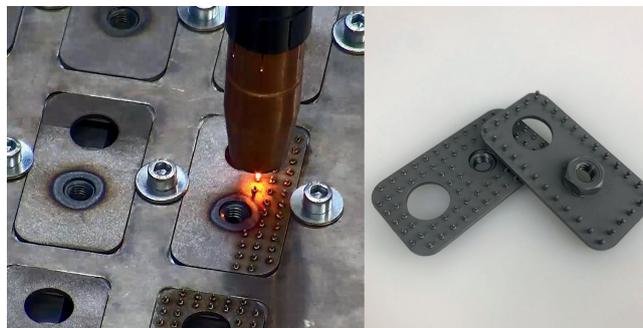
Durch CMT-Schweißen können auf den Gewindeeinlegern Pins in definierter Länge und mit verschiedenen Kopfformen angebracht werden
